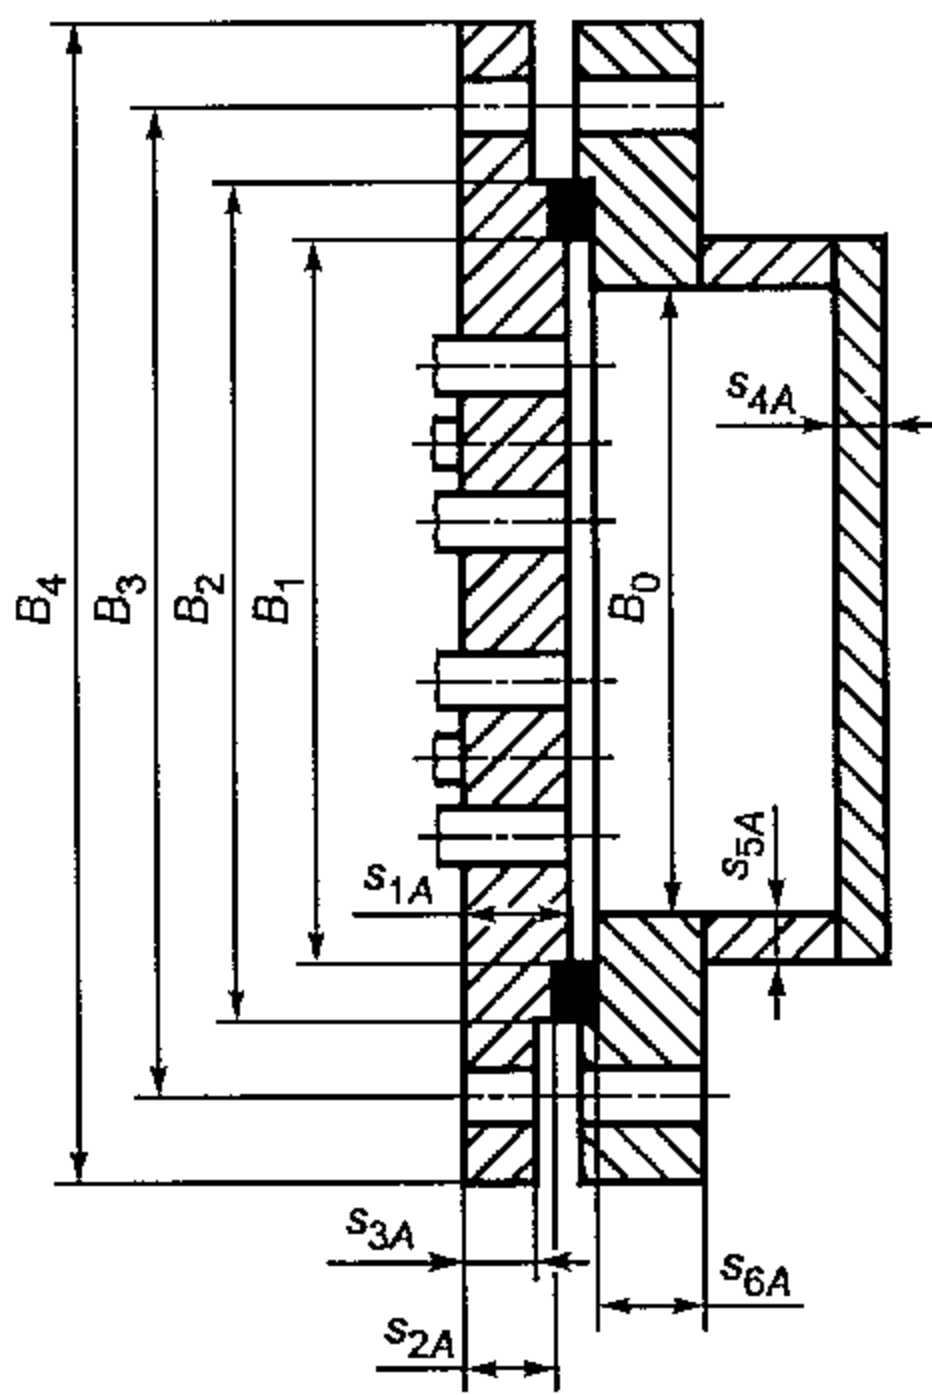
Камера разъемной конструкции со сварной крышкой
